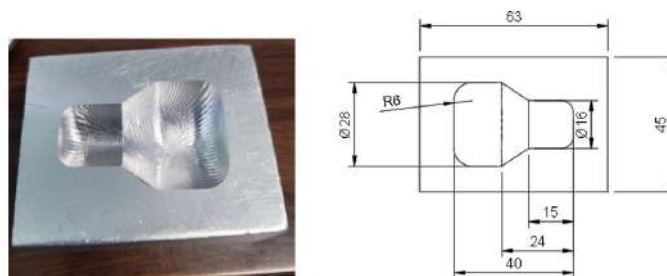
Mecnizado de pieza usando material de aluminio.
